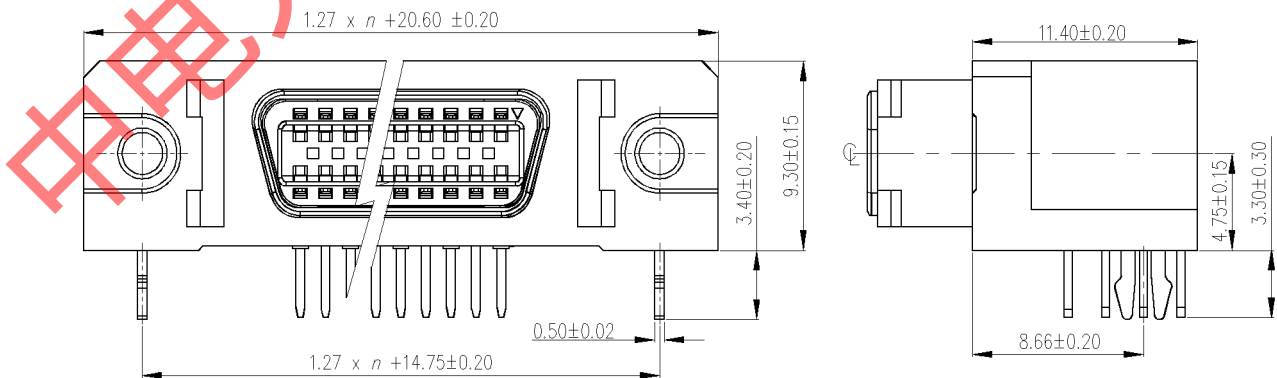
M 类型插座 90 度穿孔焊接式外形尺寸
